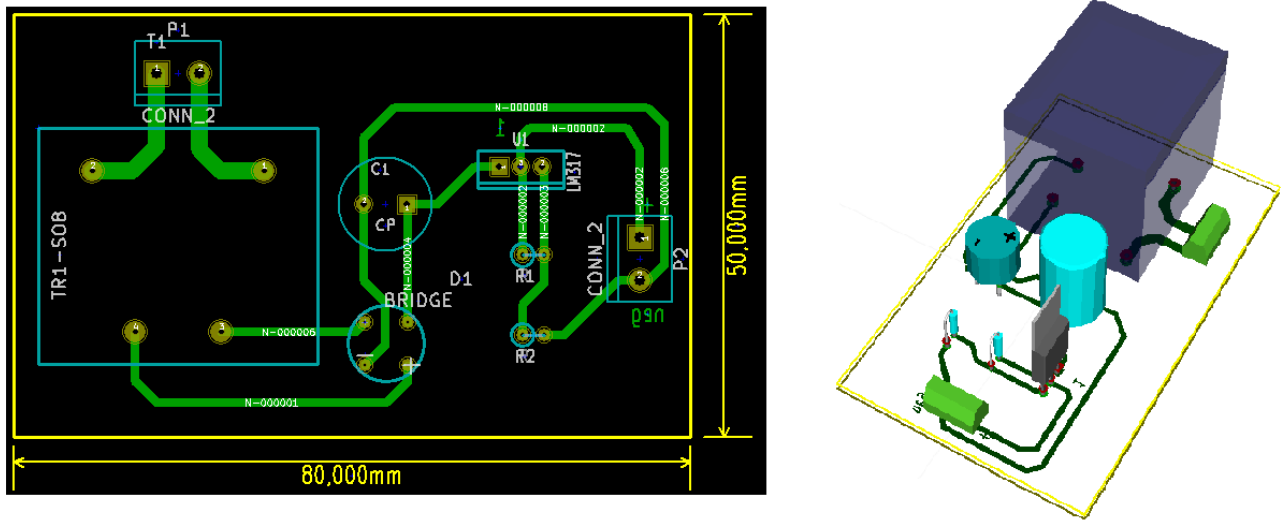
Diseño PCB y representación 3D con Pcbnew.
